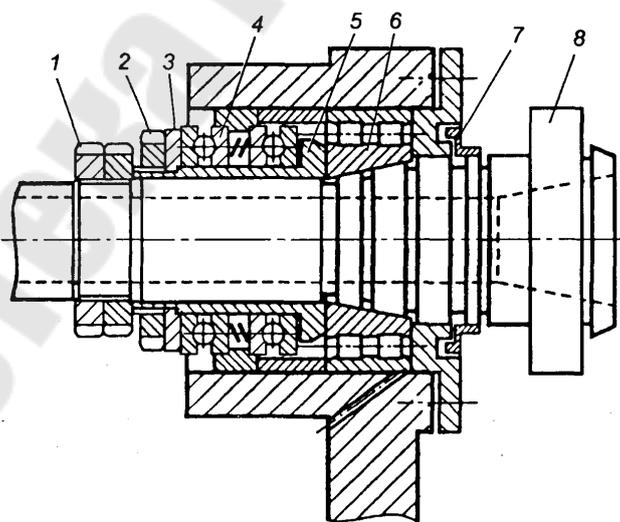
Конструкция передней опоры шпинделя токарного станка
